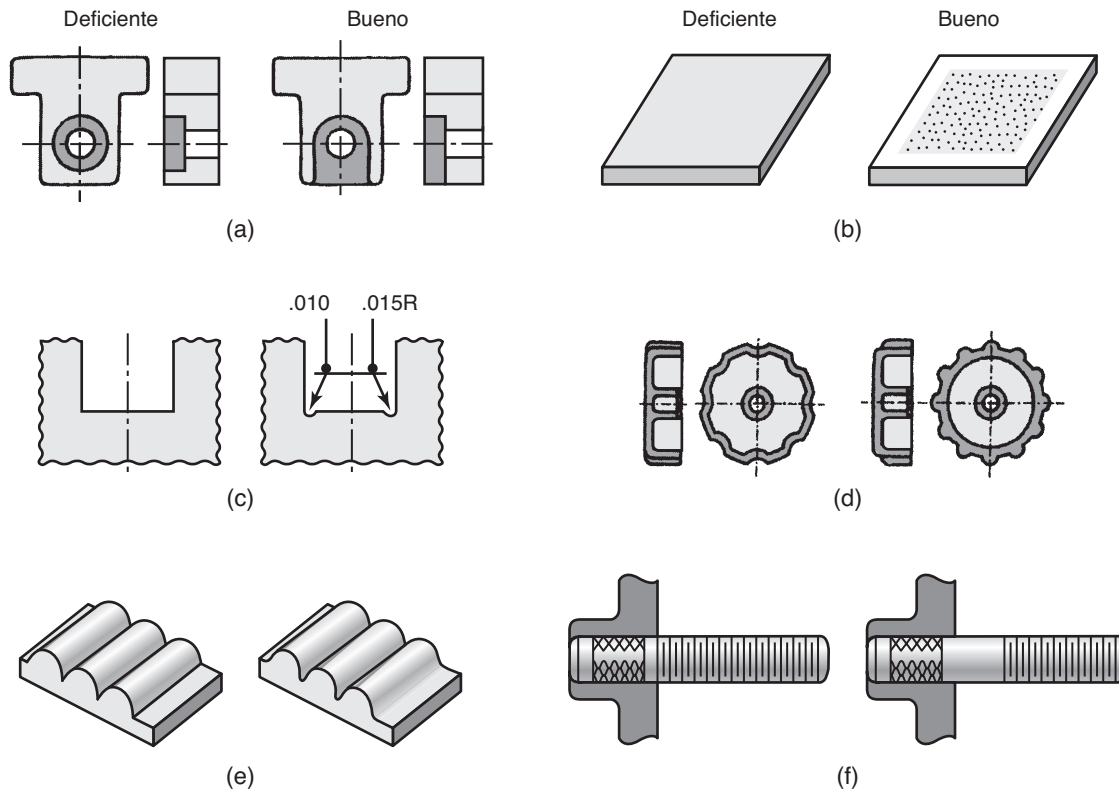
Ejemplos de diseños indeseables (deficientes) y deseables (buenos) de fundición. Fuente: Cortesía del American Die Casting Institute.
